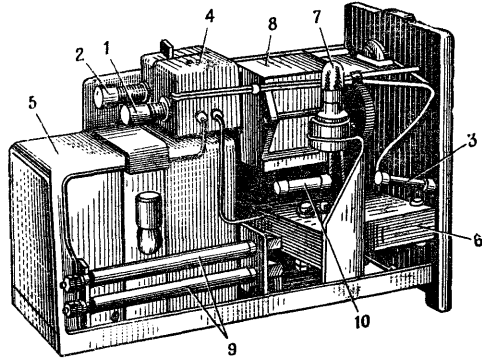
Конденсаторная подрывная машинка КПМ-2 без корпуса:
